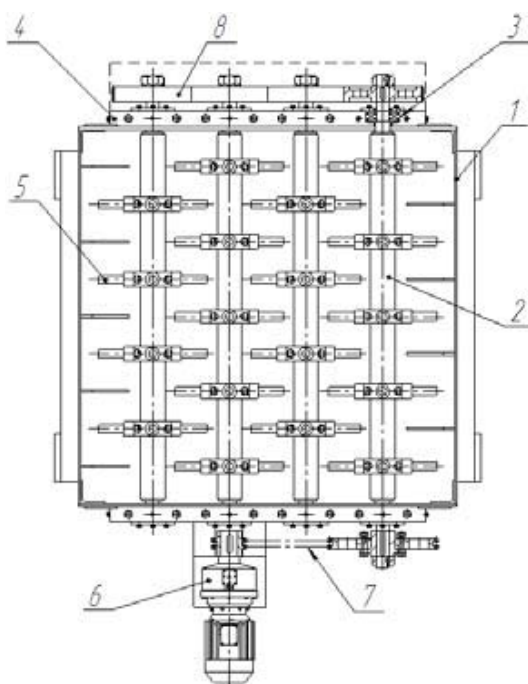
Схема царги: 1 - корпус; 2 - вал; 3 - сферический двухрядный подшипник; 4 - стакан; 5 - штыревой ворошитель; 6 - мотор-редуктор; 7 - цепная передача; 8 – синхронизирующая шестерня
